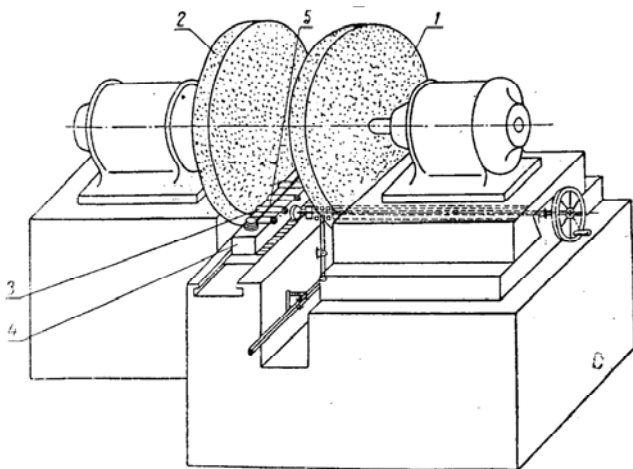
Устройство станка для двухстороннего шлифования пружин:
